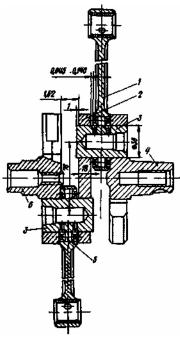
Коленчатый вал двигателя К-750 в сборе: 1 - шагун,
